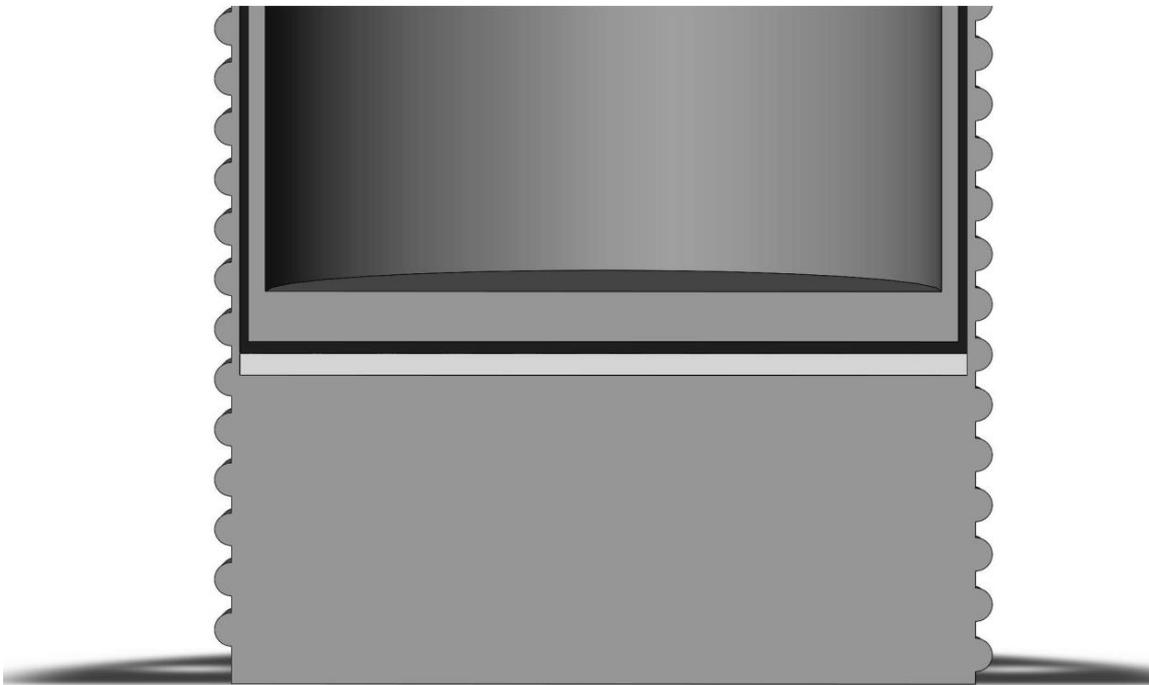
Металлическая пластина жесткости, установленная в нижнюю часть композитного корпуса
